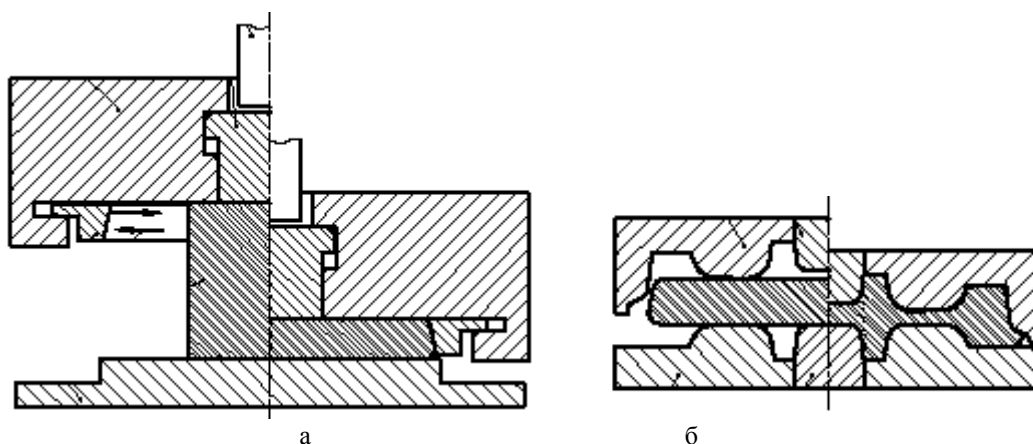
Схема осадки заготовки на плоских штампах с калибровочным кольцом (а) и окончательной штамповки (б)
